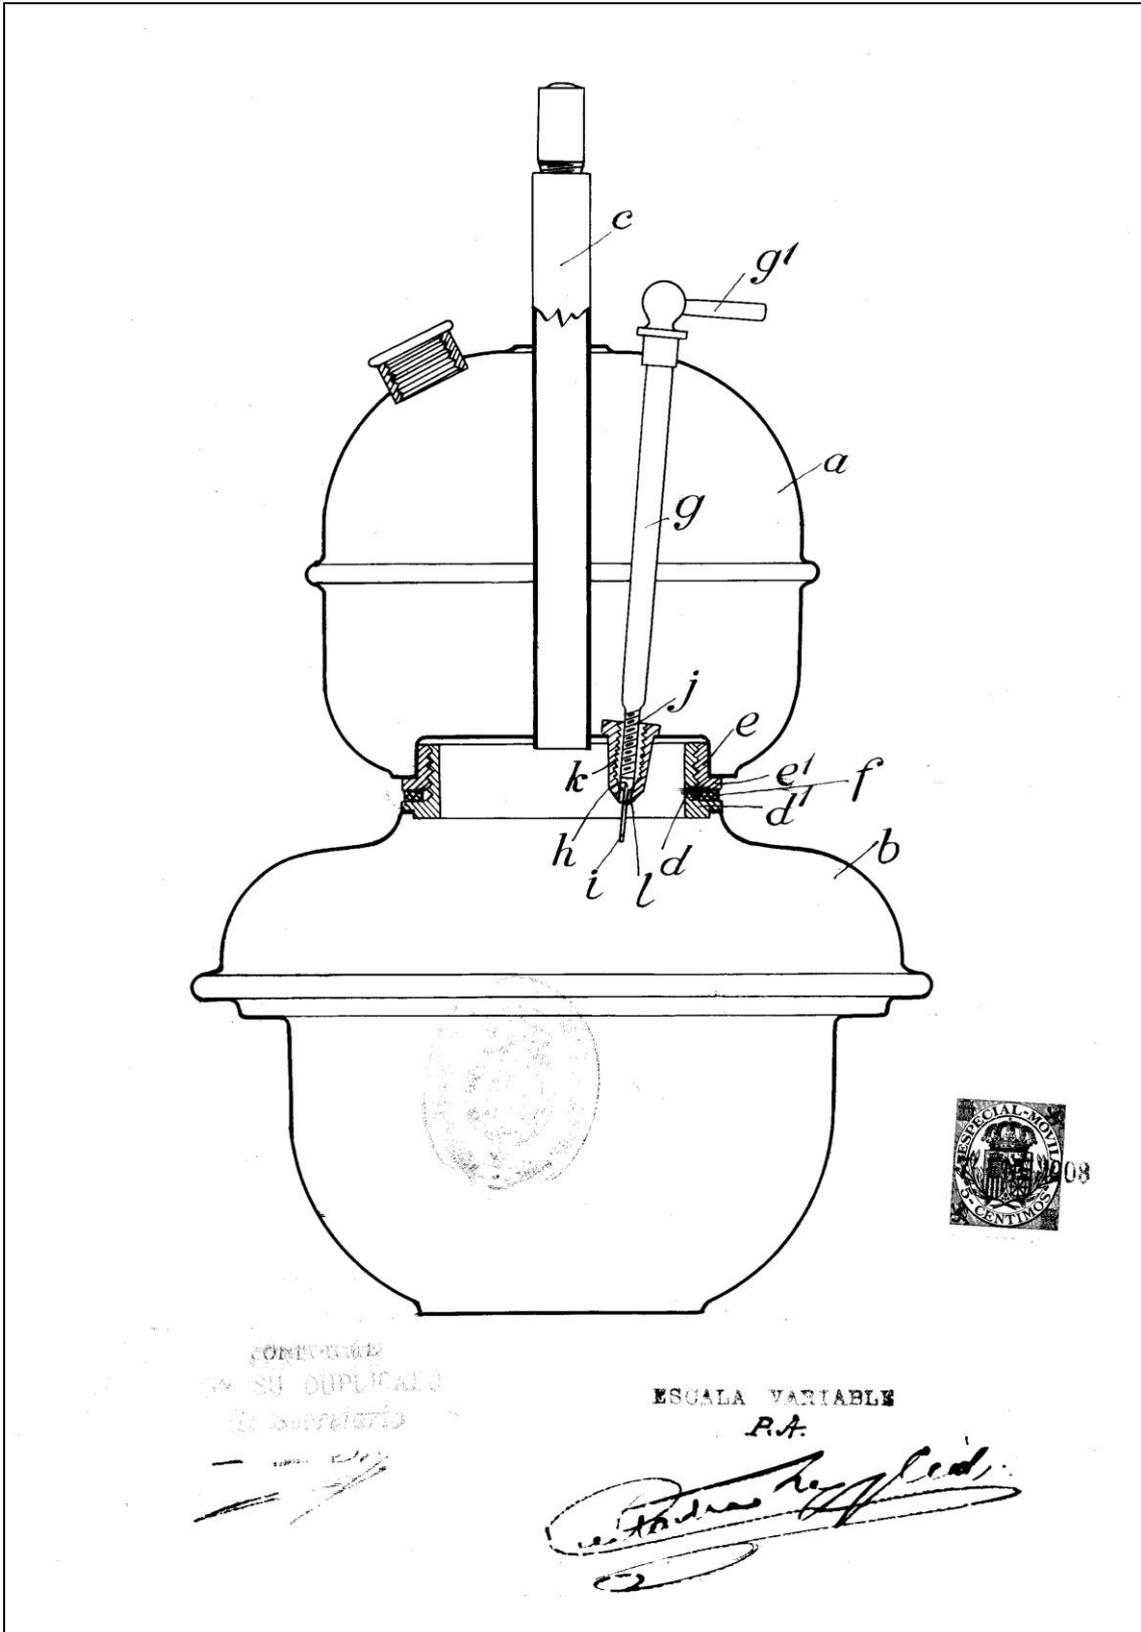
Patente nº 42421 (Arch. J. M. Sanchis)
